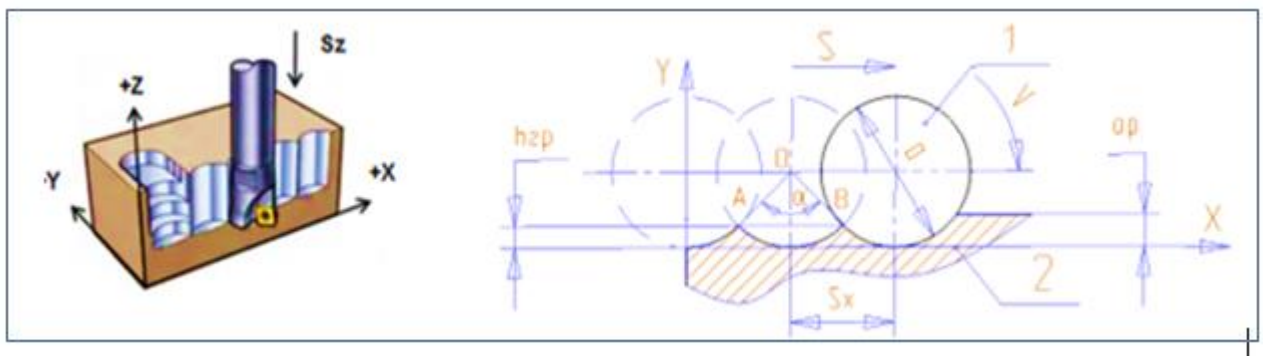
Компьютерная модель формирования неровности при плунжерном фрезеровании: 1 – контур фрезы; 2 – обрабатываемая поверхность;  $V$  – направление вращения фрезы;  $S$  – направление подачи фрезы вдоль обрабатываемой поверхности;  $h_{гр}$  – высота «гребешка»;  $a_p$  – глубина резания;  $S_x$  – величине однократного смещения фрезы вдоль обрабатываемой поверхности;
